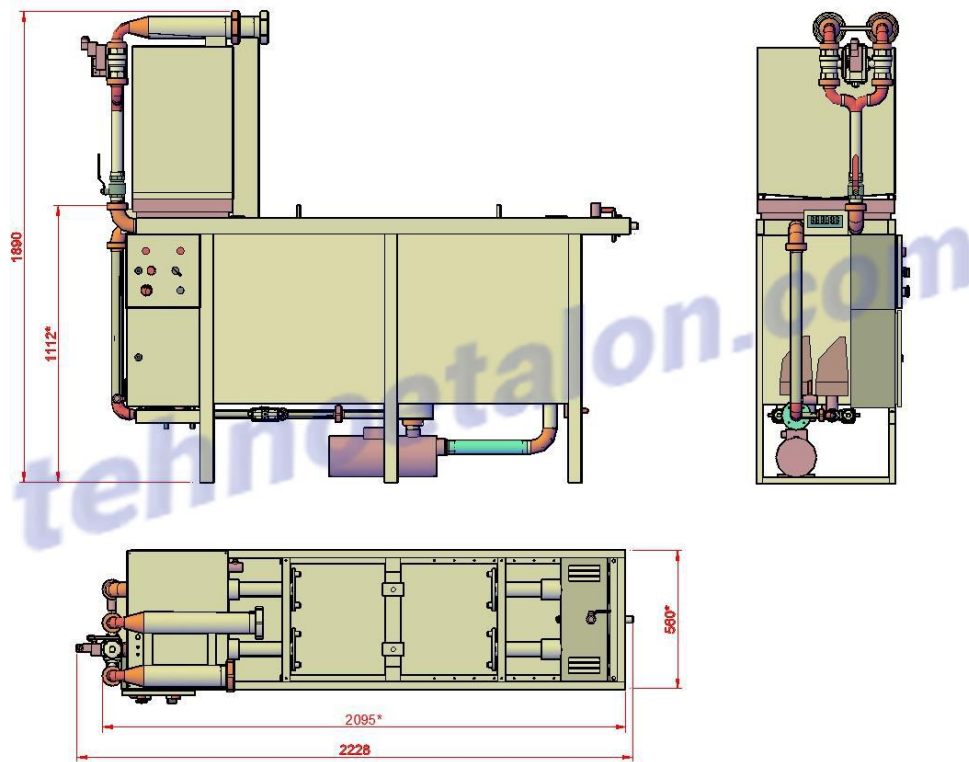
Габаритные * размеры проливной установки АС-50 (* транспортные размеры)
